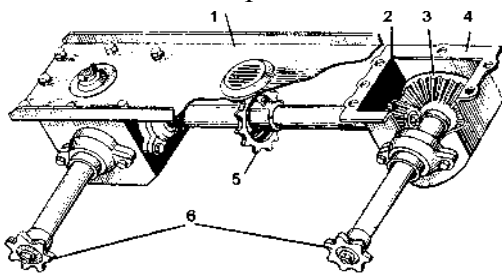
РЕДУКТОРЫ ПРИВОДА ПИТАТЕЛЕЙ
